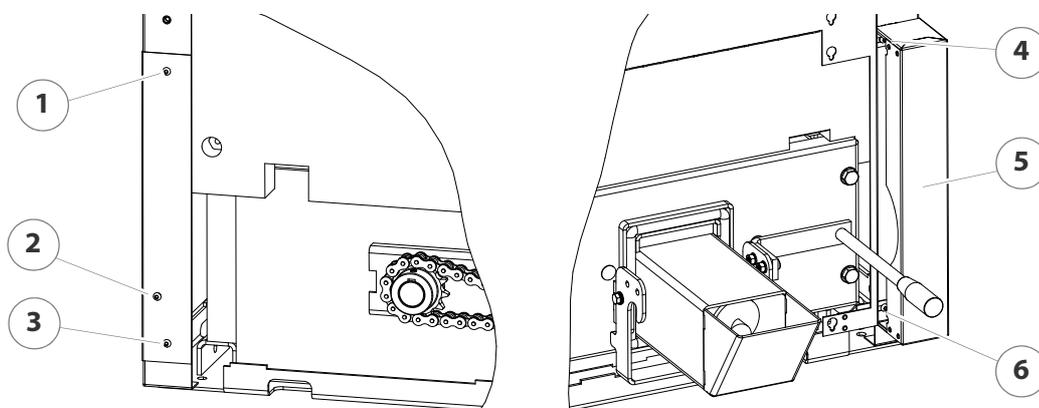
/38 - Montage des jaquettes latéral côté conduit de fumée, en bas
